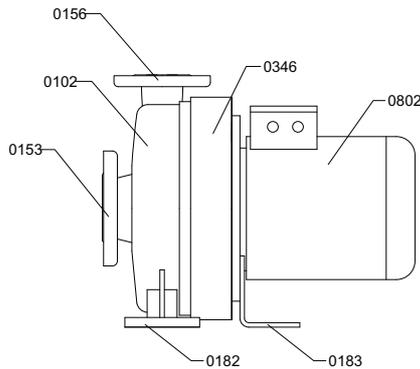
MAXA Bloc con motore di dimensione fino a 112
